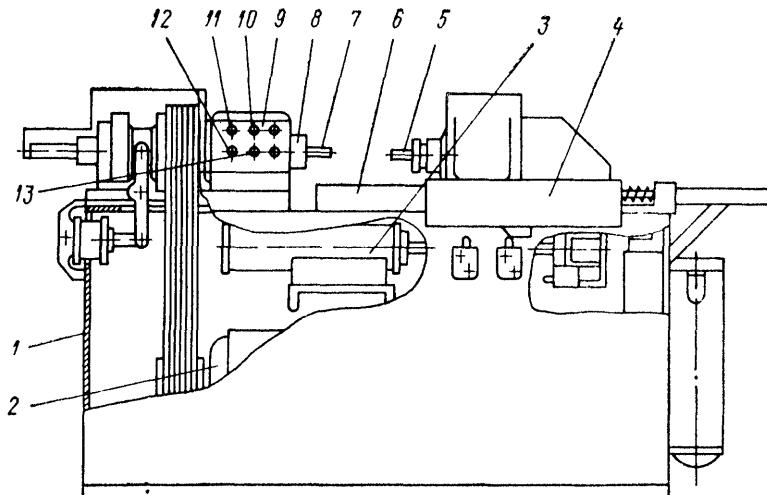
Специальный сварочный полуавтомат модели МФ-327:
